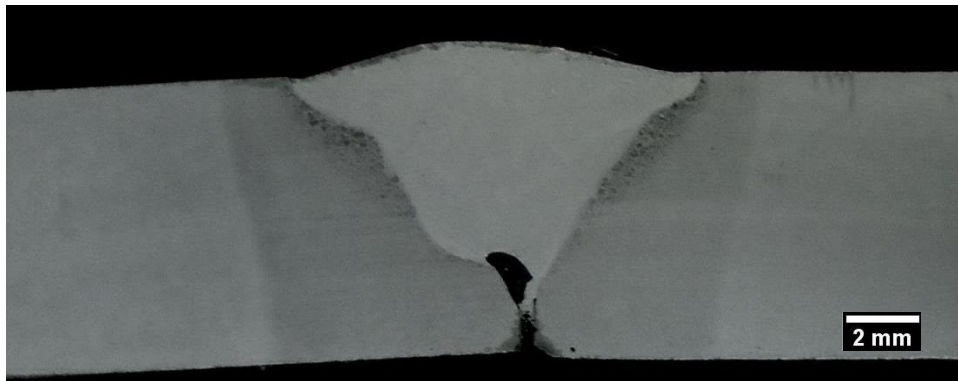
Condição (C). Soldagem com tratamento vibracional de alívio tensão (Pós soldagem).
